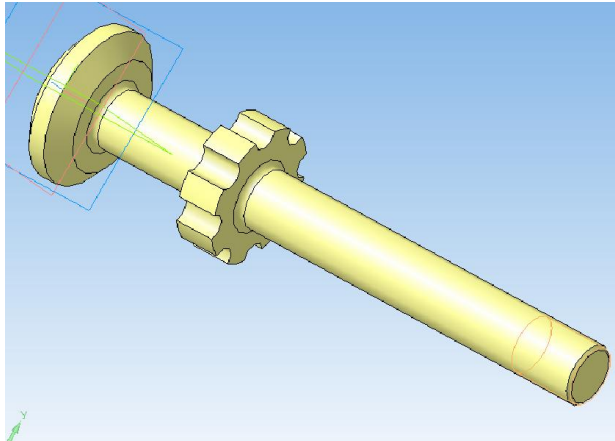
Клапан пусковой, детализовка 3D сборки
